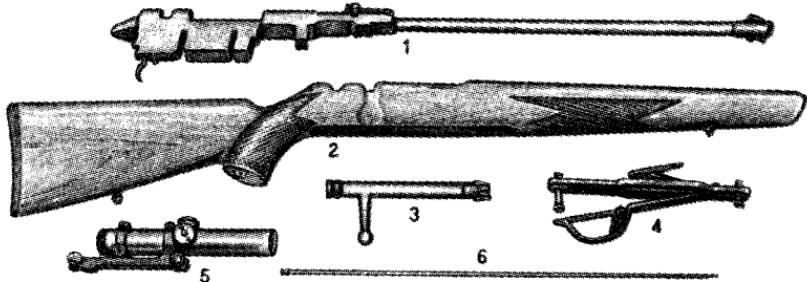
Детали и узлы магазинного карабина «Лось»: 1 - ствол со ствольной коробкой в сборе; 2 - ложа; 3 - затвор; 4 - магазин с предохранительной скобой; 5 - оптический прицел с кронштейном; 6 - шомпол.
